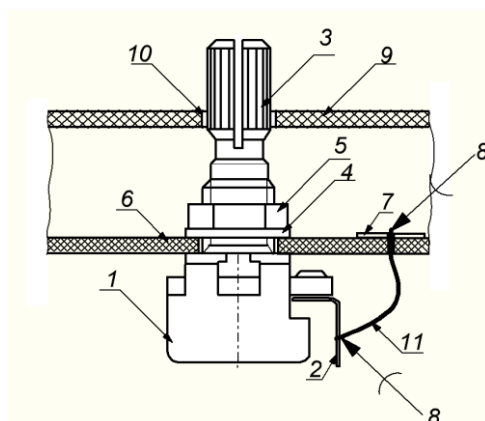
Фрагмент варианта расположения переменного резистора типа WH186-1A-1 в конструкции изделия с фиксацией на печатной плате: 1 – корпус резистора; 2 – выводы; 3 – ось переменного резистора под ручку; 4 – шайба; 5 – гайка; 6 – плата; 7 – контактная площадка; 8 – паяное соединение; 9 – лицевая панель крышки; 10 – отверстие в крышке корпуса для прохода оси резистора; 11 – соединительный проводник
